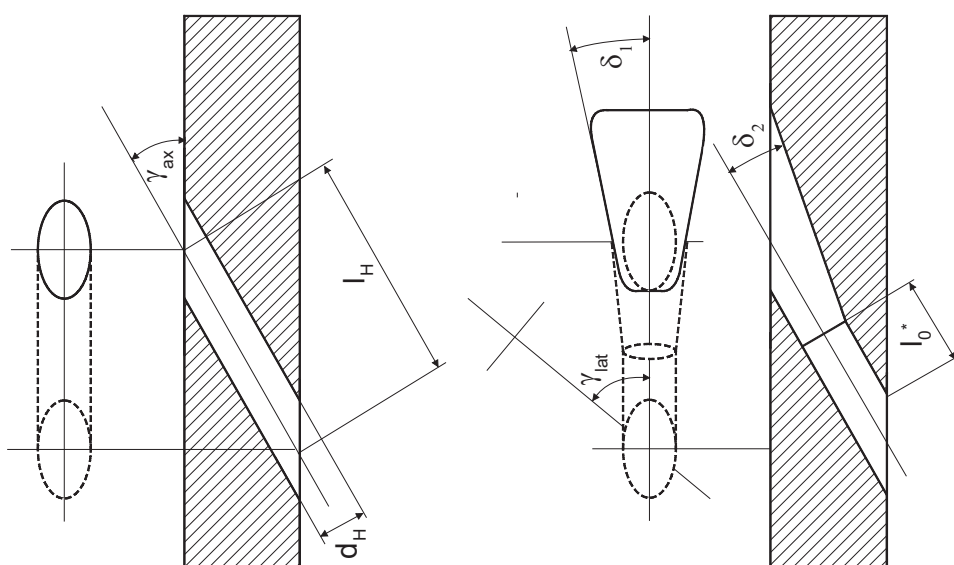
Bohrungsgeometrie T106–300–4, links: zylindrische Grundbohrung, rechts: Fan-Shaped Bohrung mit Laid-Back
